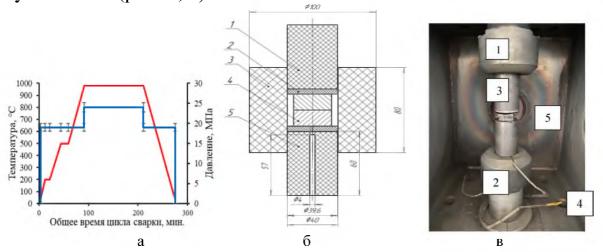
а) циклограмма диффузионной сварки на оборудовании SPS 10–3; б) схема размещения заготовок: 1 — верхний пуансон; 2 — корундовая вставка; 3 — матрица; 4 — свариваемые заготовки; 5 — нижний пуансон с технологическим отверстием под термопару; в) схема размещения заготовок перед электрической сваркой сопротивлением: 1 — гидравлический цилиндр, 2 — графитовая вставка, 3 — пуансоны, 4 — термопара, 5 — свариваемые заготовки.
